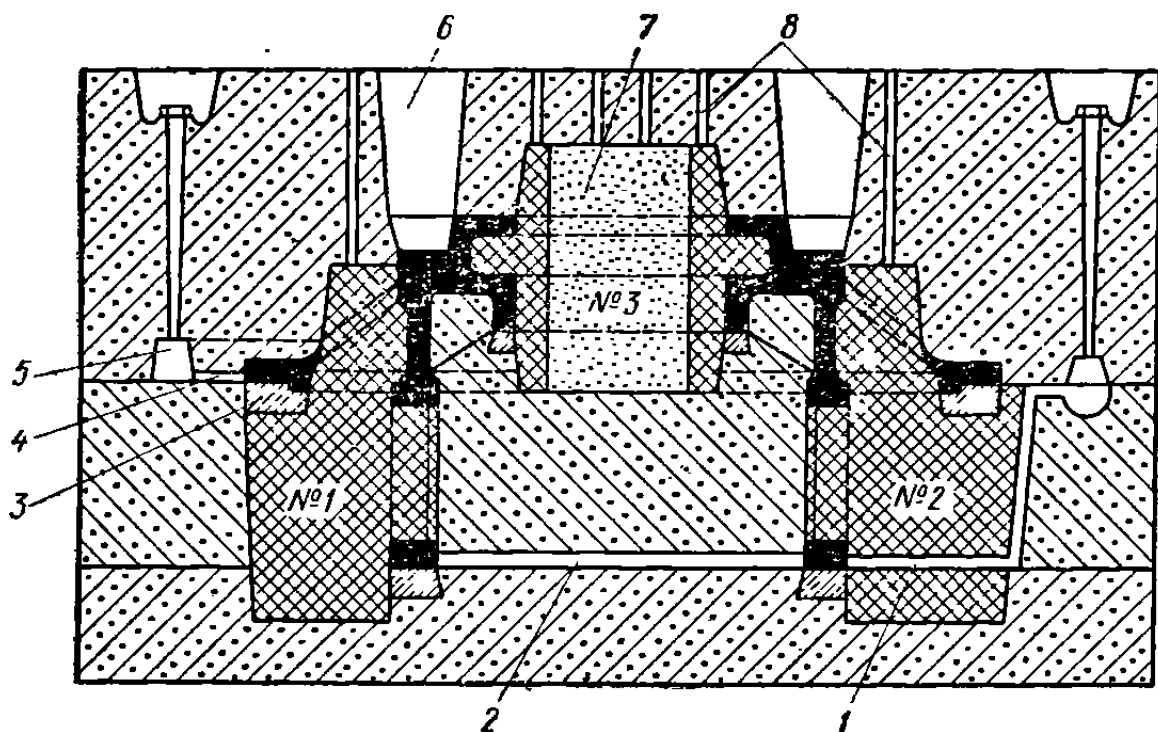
Схема литейной формы для отливки сплава АЛ9
